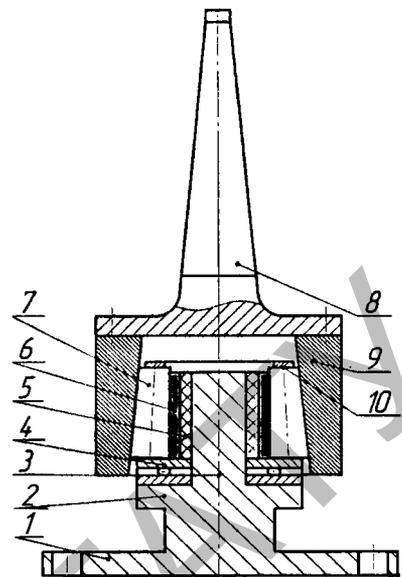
Установка для многороликовой обкатки бронзовых подшипников скольжения:
